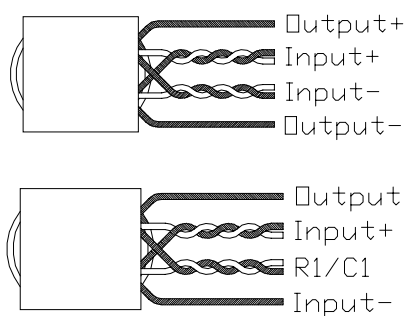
Detalles de construcción de los transformadores T2 (arriba) y T3 (abajo)
